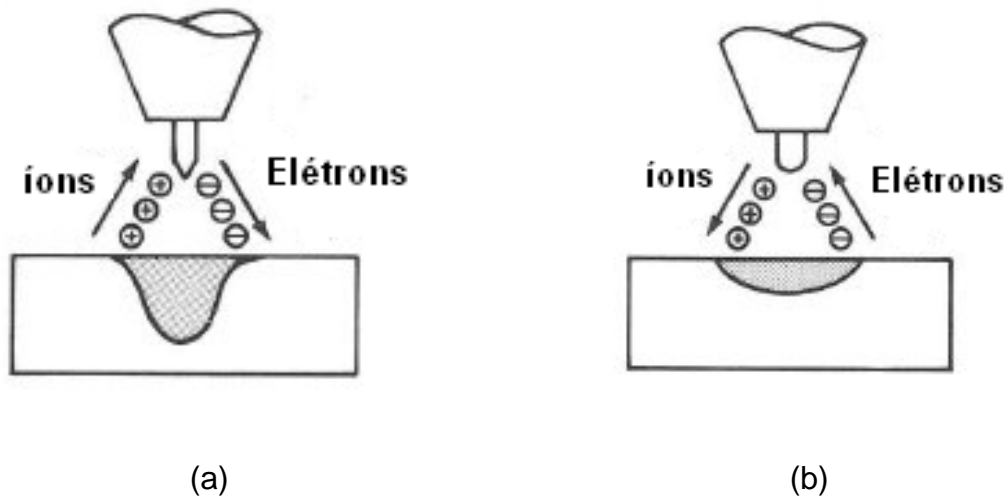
Processo de soldagem GTAW utilizando: a) CCPD e b) CCPR [17].
